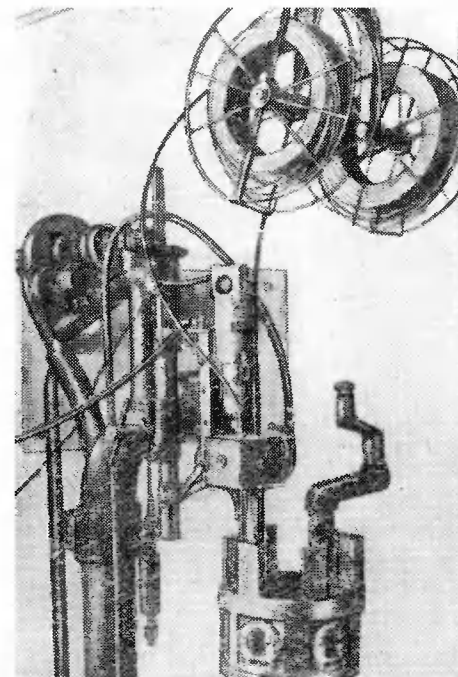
Установка металлизатора для восстановления внутренних поверхностей головки станка
